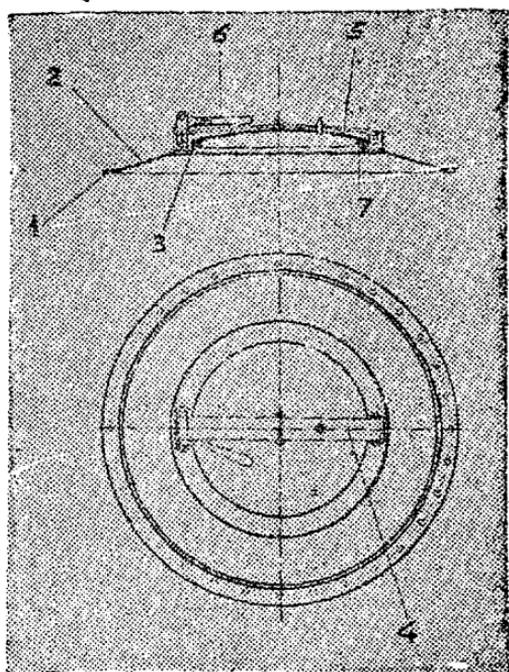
Крышка газогенератора в сборе: 1—фланец; 2—конус; 3—горловина загрузочного люка; 4—ressора; 5—крышка загрузочного люка наружная; 6—рычаг; 7—прокладка.
